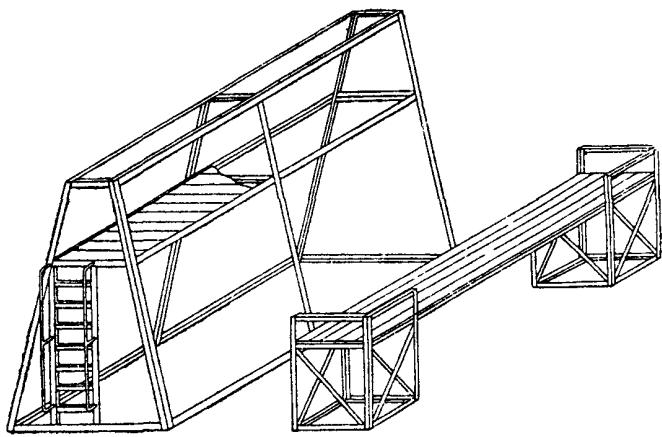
Общий вид вертикального стенда для сборки стеклопанелей
